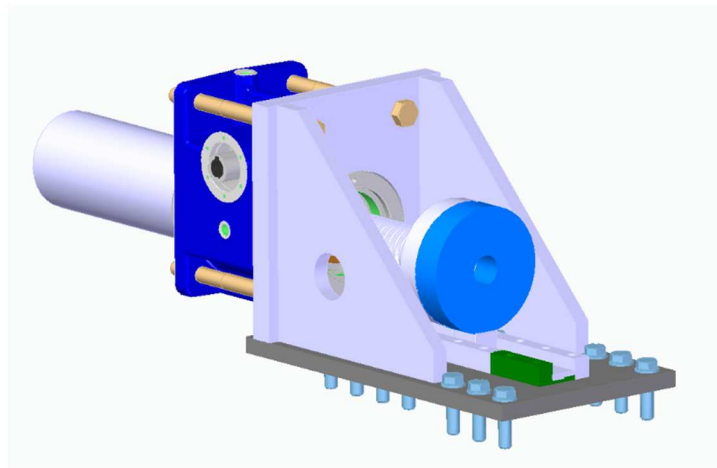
Sotto-assieme sistema di caricamento, disegno CAD 3D.
